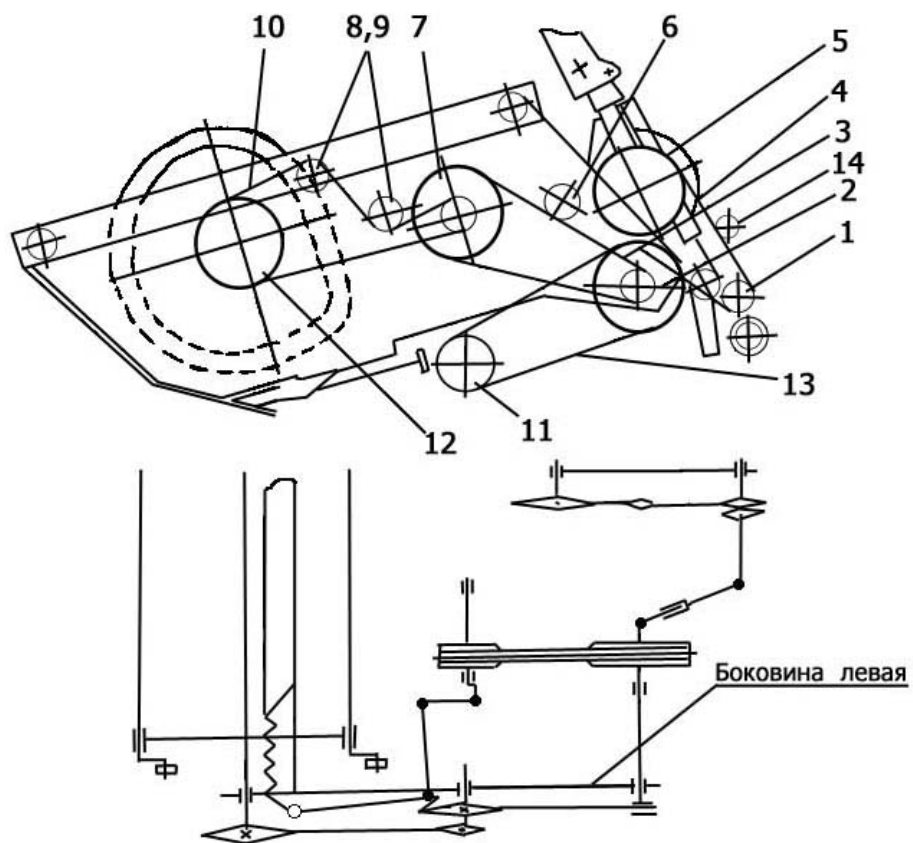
Схема кинематическая жатки для уборки трав (вид слева)
